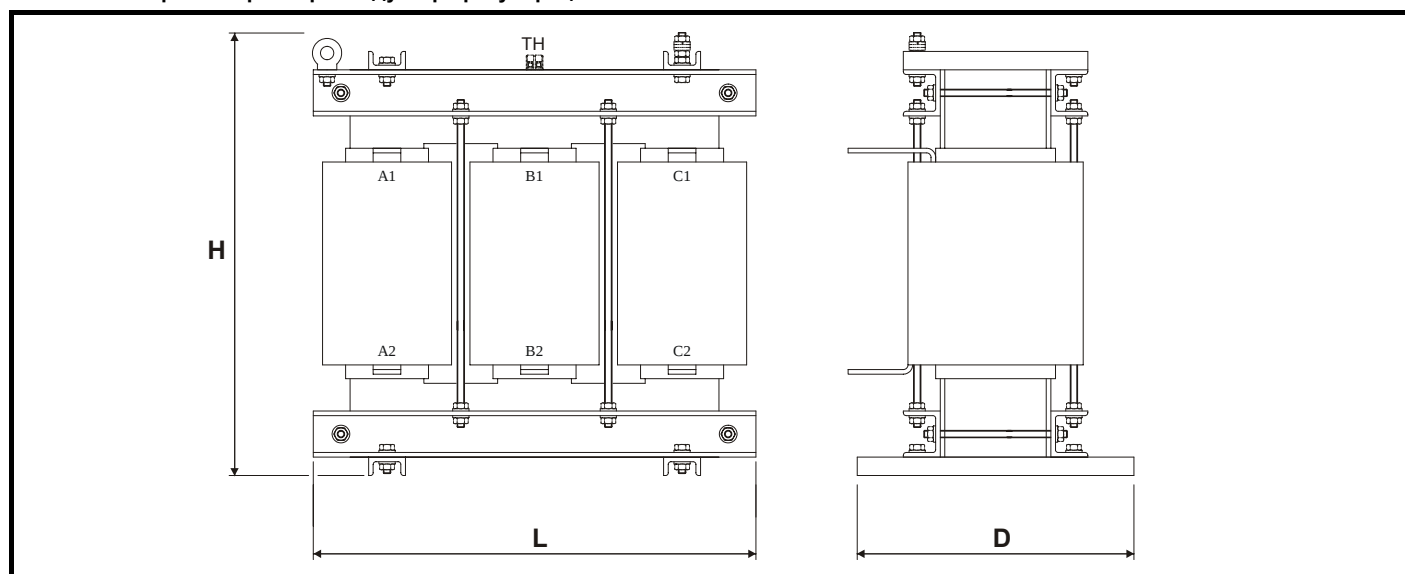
Габаритные размеры индуктора рекуперации типа 3
